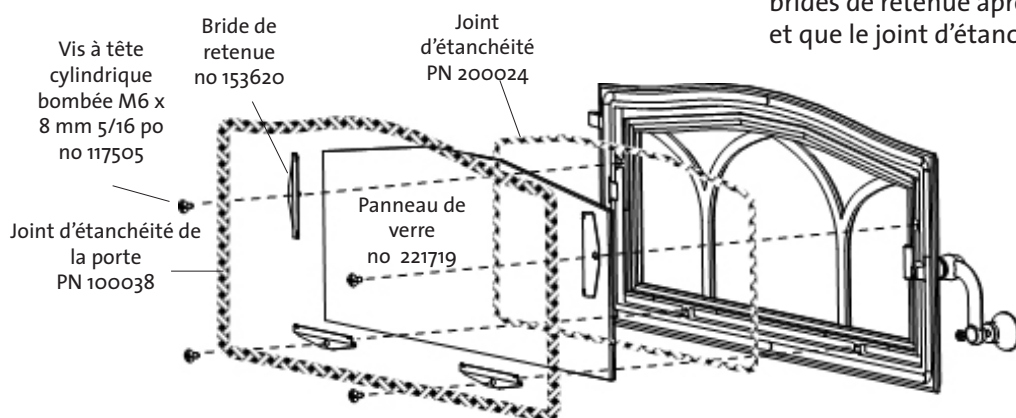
Pièce de remplacement de la porte de verre et des joints d'étanchéité.
